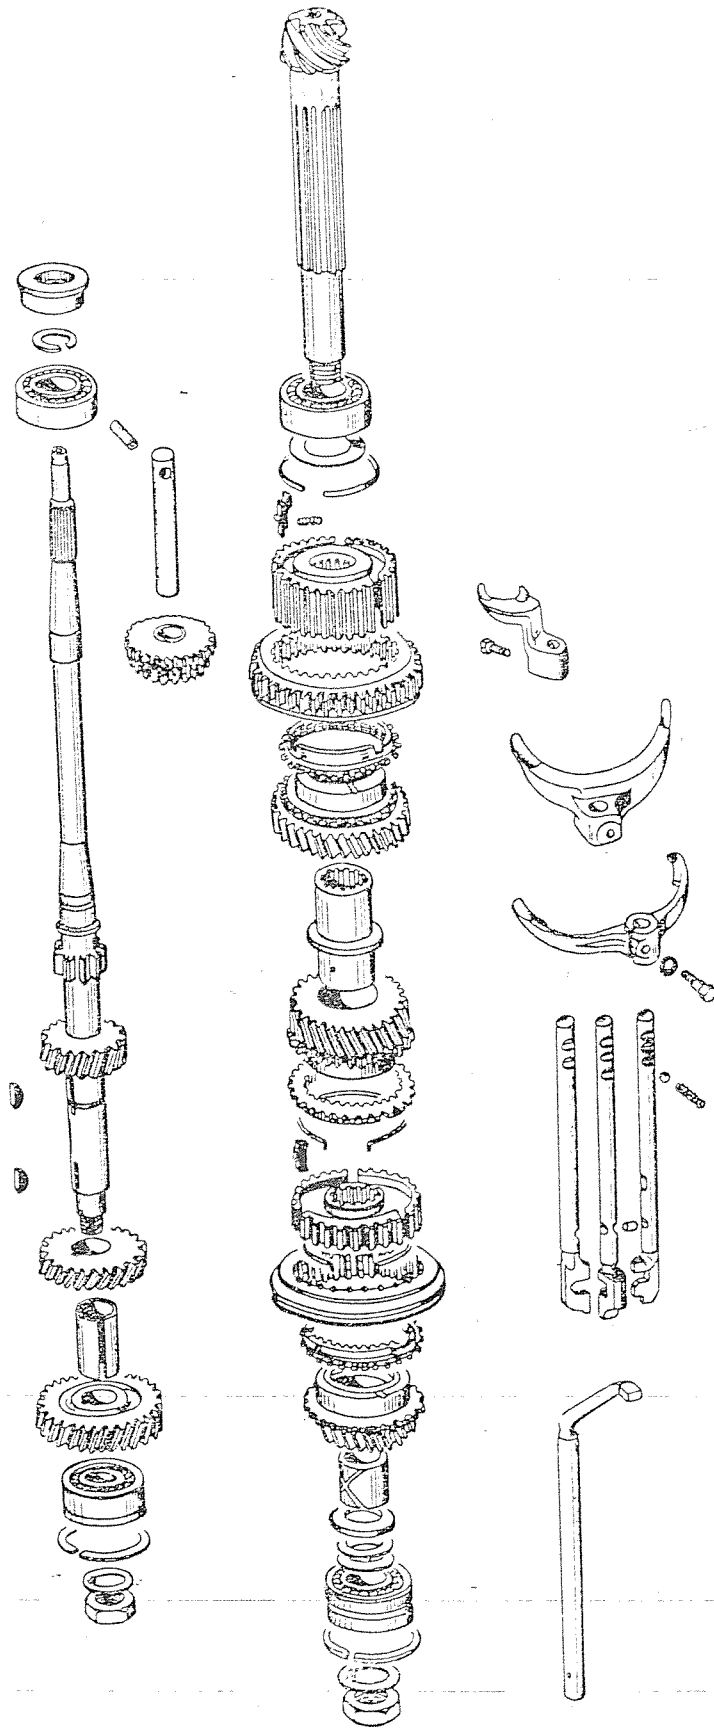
Orden de sucesión de las operaciones para el armado de los engranajes de la caja, bujes, ejes y cojinetes (caja sincronizada).
